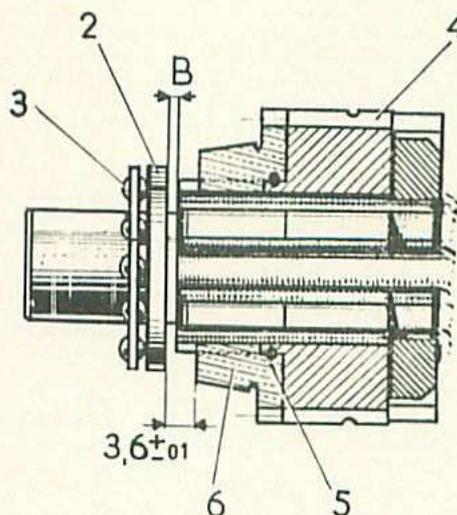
Ensemble du pignon de 3<sup>e</sup>.
